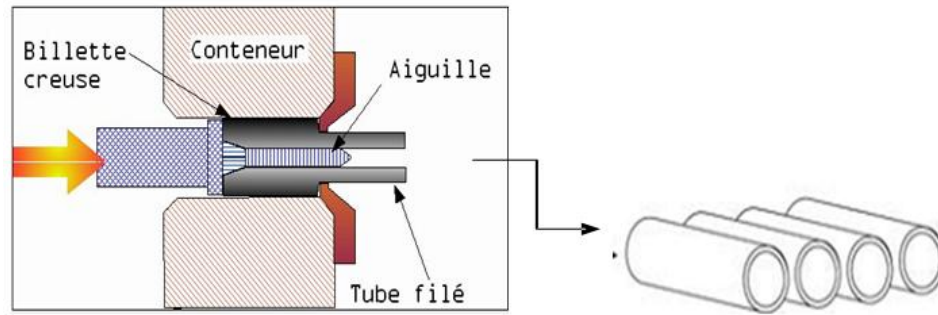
Fabrication de pipe sans soudure
